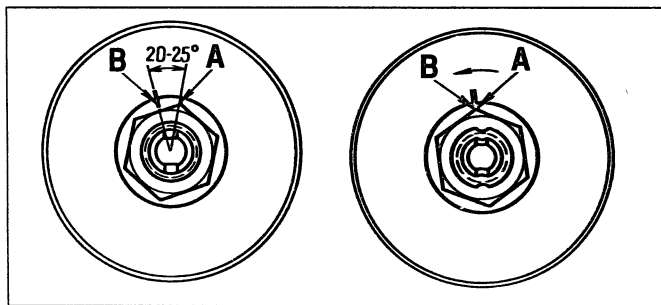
Затягивание и регулировка подшипников ступицы переднего колеса: А – кромка гайки; В – метка на шайбе
